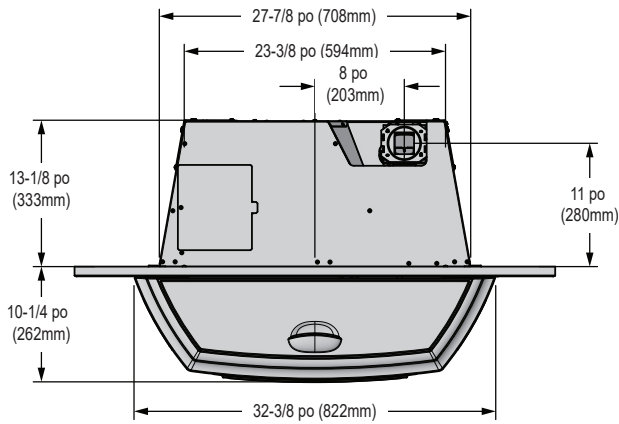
Vue de dessus avec ensemble de panneaux de fonte
